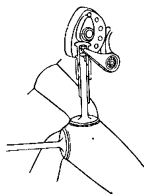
Конструкция клапана двигателя спортивного автомобиля «Мерседес-Бенц» модель «SLR»
